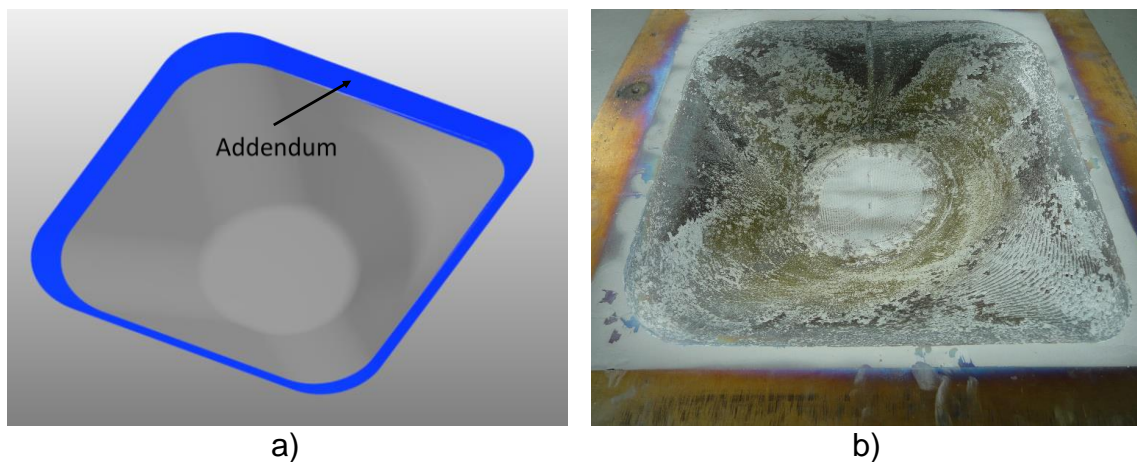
Geometría con addendum: a) CAD; b) Pieza fabricada.
